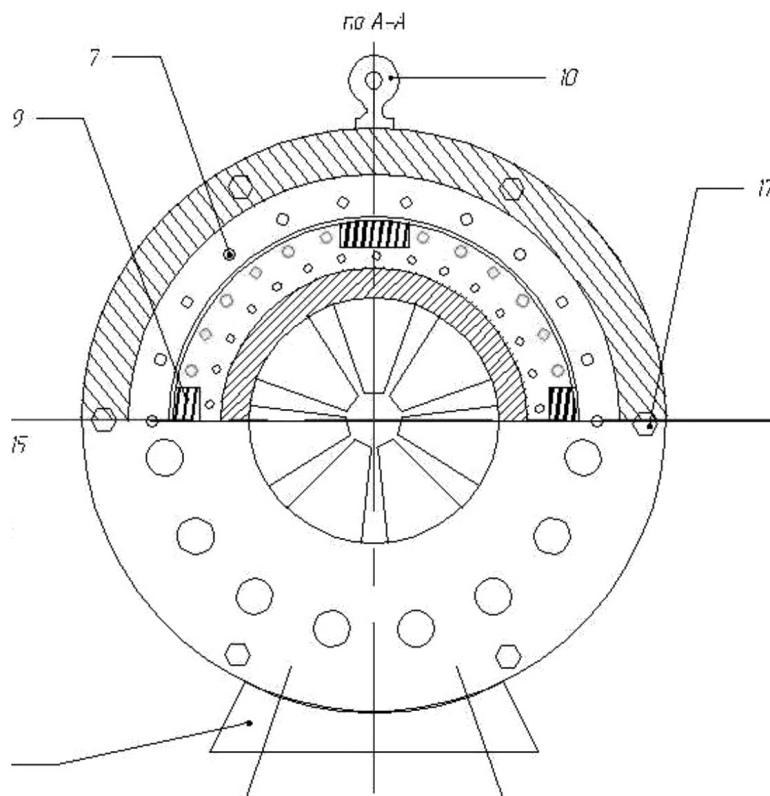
Поперечный разрез: 7 – обмотка статора, 9 – постоянные магниты, 10 – рым-болт, 17 – болты крепления подшипниковых щитов, 18 – рама опорная
